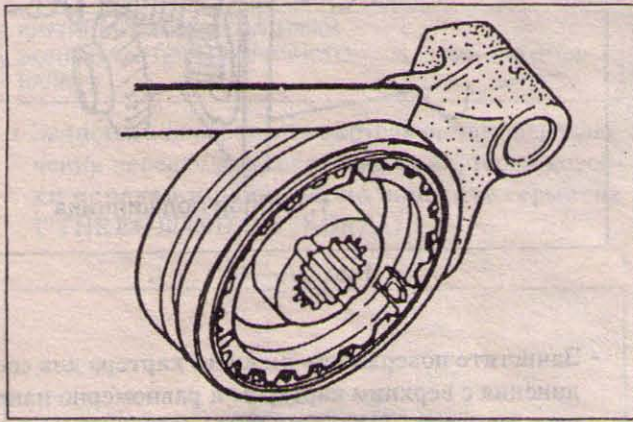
А—39 ПРОВЕРКА ЗАЗОРА
